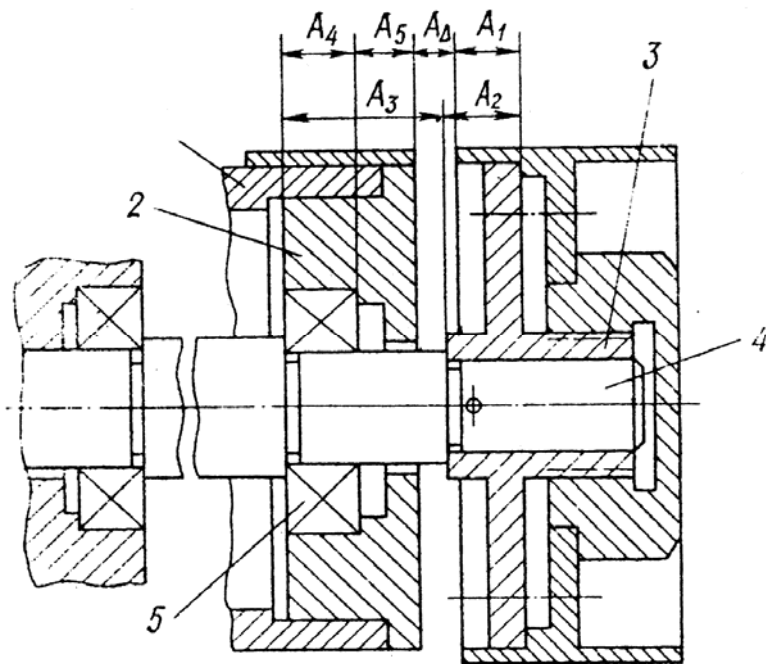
Узел подшипникового соединения: 1 – корпус; 2 – крышка; 3- фланец;
